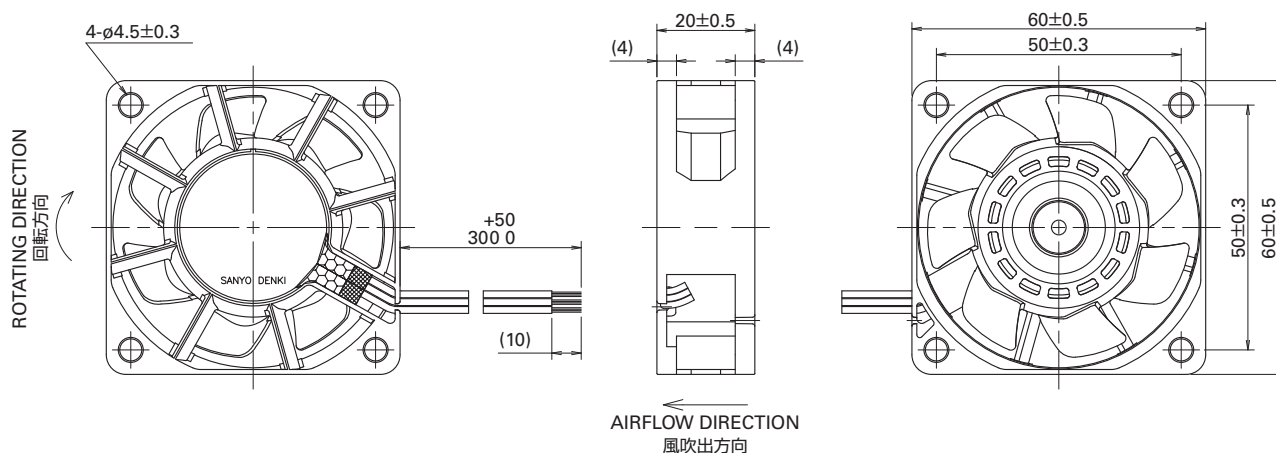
「San Ace 60WF」寸法緒元 (単位: mm)
